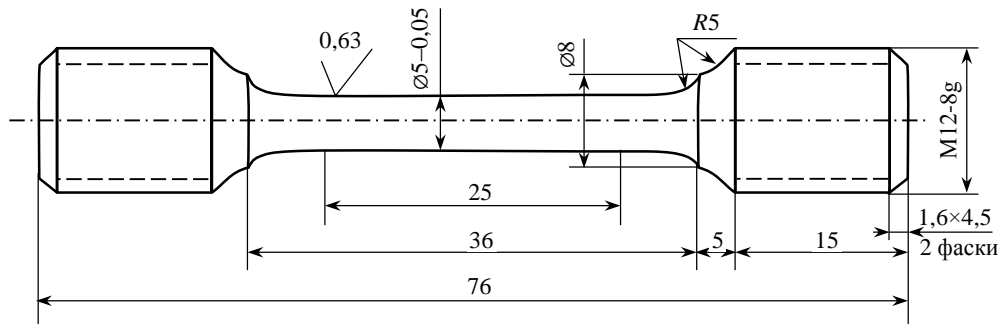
Эскиз образца из сталей 38Х2МЮА и 30Х3МА
